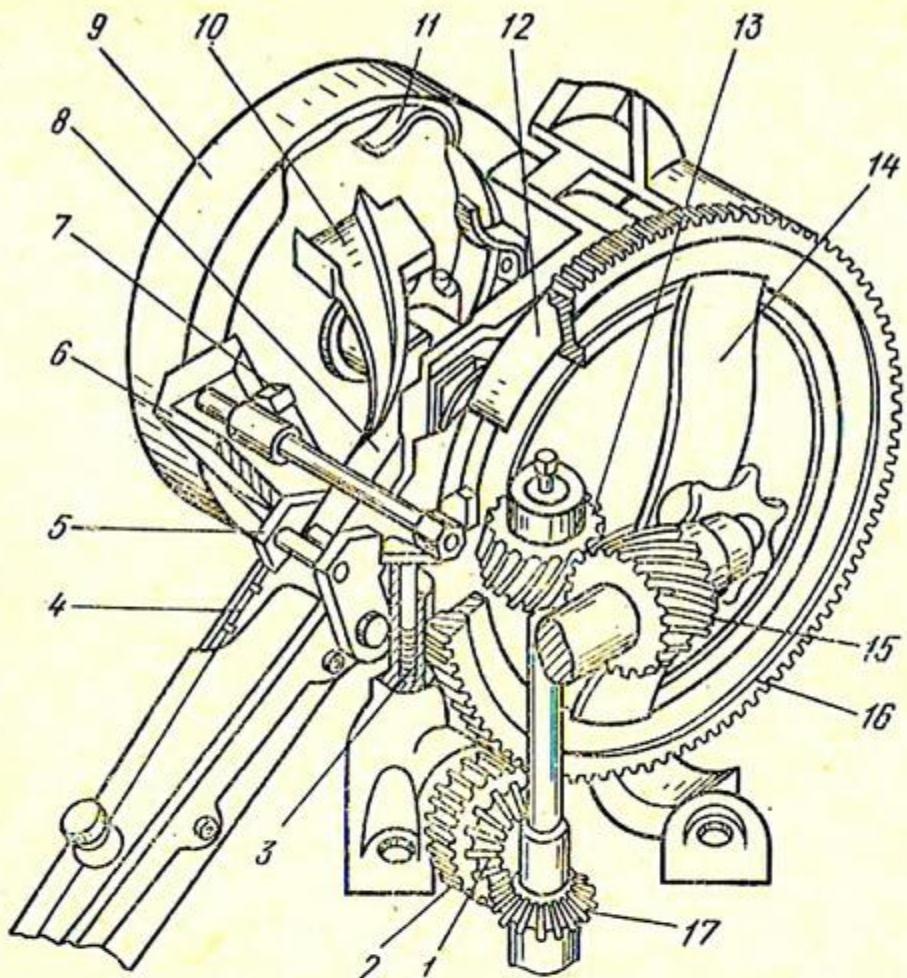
Механизм подачи гвоздей машины 3В-3-О
